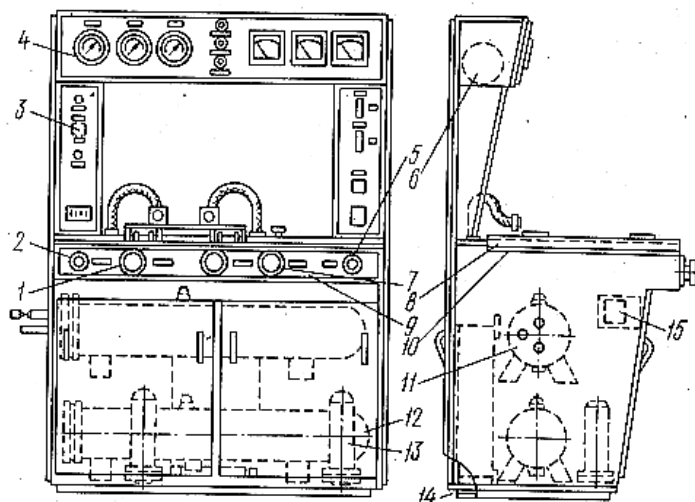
Стенд обкатки бессальникового компрессора на хладагенте R12:
